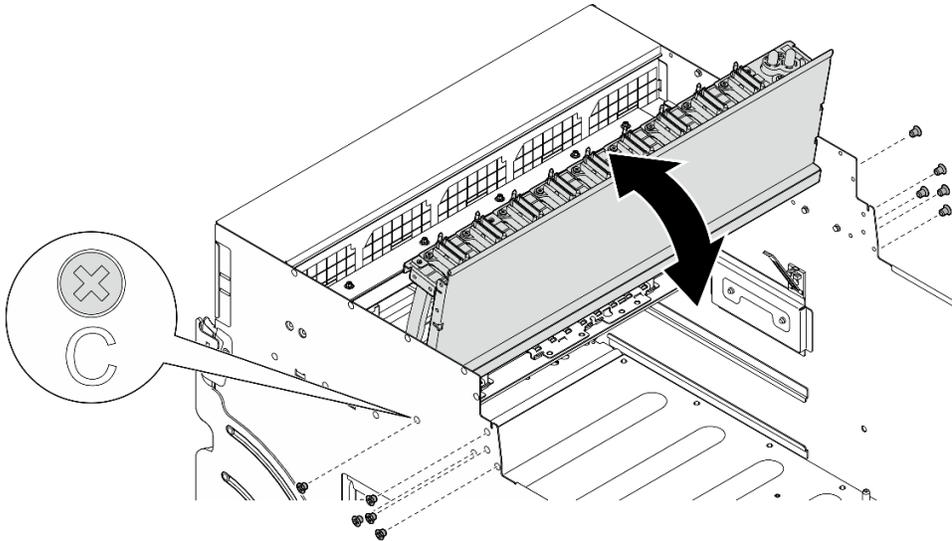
Giro del arnés de cables del conmutador PCIe frontal
